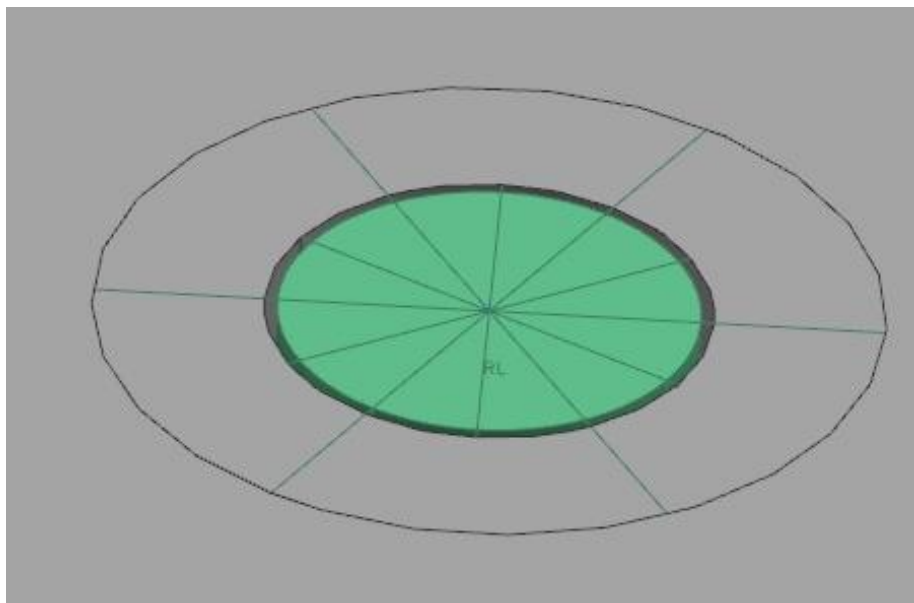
Detail radiální síly od ložiska působící na převodovou skříň
